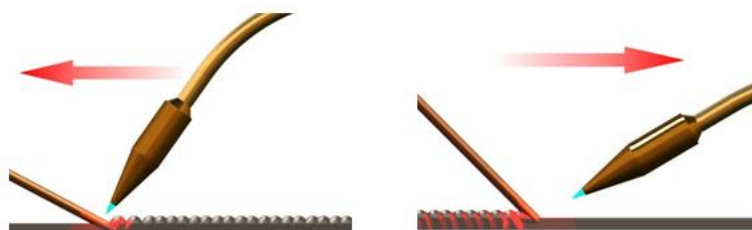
Técnicas de soldadura (para a esquerda, à esquerda e para a direita, à direita)
